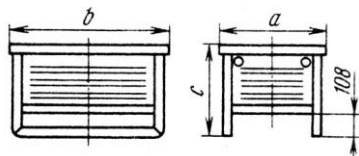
Схемы ящичных поддонов конструкции НПО "Оргстанкинпром"
